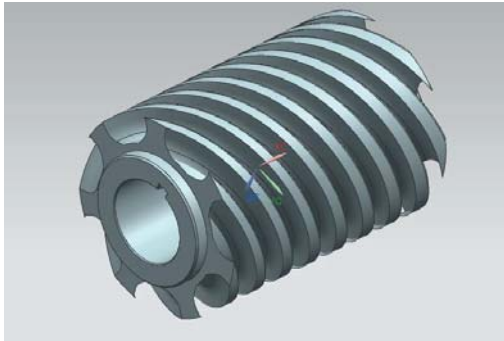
Модель инструмента червячного типа со сплошными винтовыми режущими кромками
